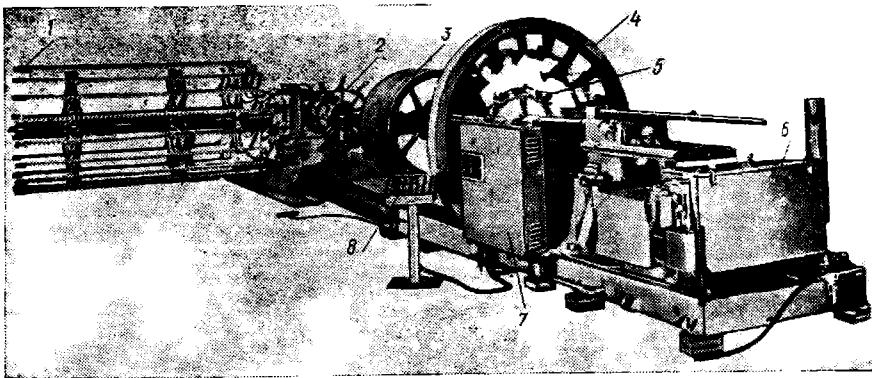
Станок для сборки крупногабаритных покрышек:
